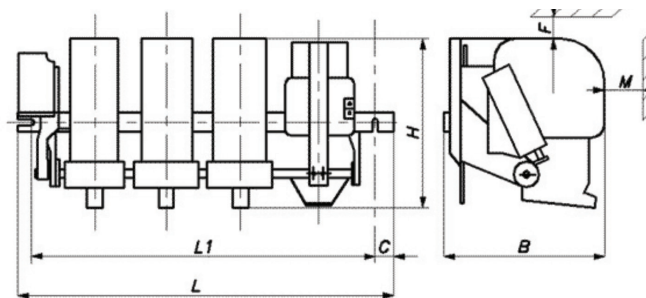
общий вид, габаритные и установочные размеры контакторов серии КТ-6000
